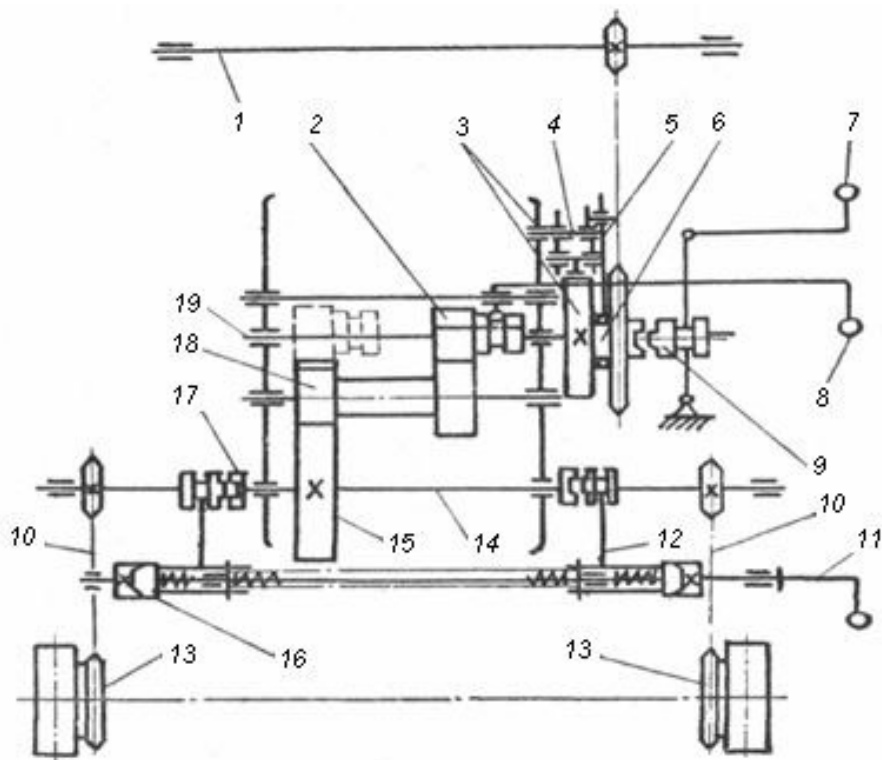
Схема механизма самопередвижения: 1 – ведущий вал; 2 – шестерня; 3 – храповое колесо; 4 – каретка; 5 – шатун; 6 – эксцентрик; 7 – рычаг; 8 – рукоятка реверса; 9, 17 – кулачковые муфты; 10 – цепь; 11 – рукоятка; 12 – вилка; 13 – звёздочки; 14 – выходной вал редуктора; 15 – зубчатое колесо обратного хода; 16 – кулачк; 18 – зубчатый блок прямого хода; 19 – приводной вал.
